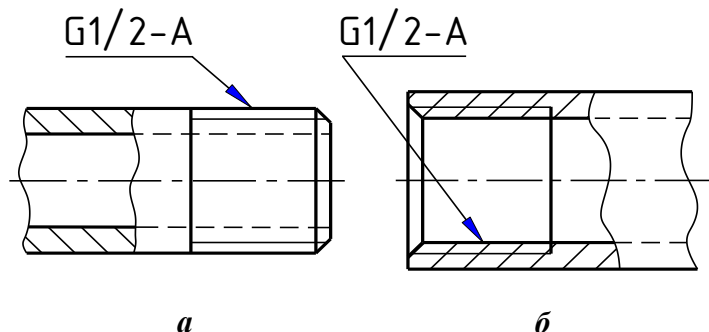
Применение *штриховых* и *тонких линий* при изображении трубной цилиндрической резьбы и нанесении ее размеров: *а* – наружной резьбы; *б* – внутренней резьбы (в обоих случаях в обозначении резьбы свинчиваемых деталей в дюймах указывается диаметр проходного отверстия в трубе, на которой выполнена наружная резьба, то есть изображенной слева)
